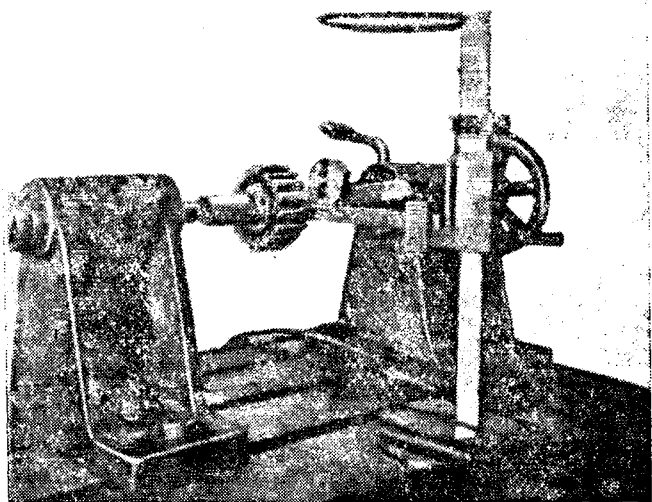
Установка фрезы в оправке на центрах для измерения переднего угла
